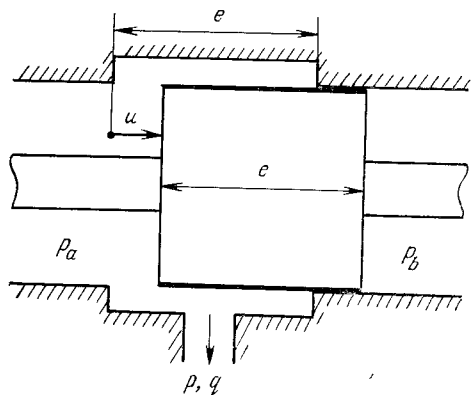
Фрагмент схемы клапана без запаса перекрытия.
